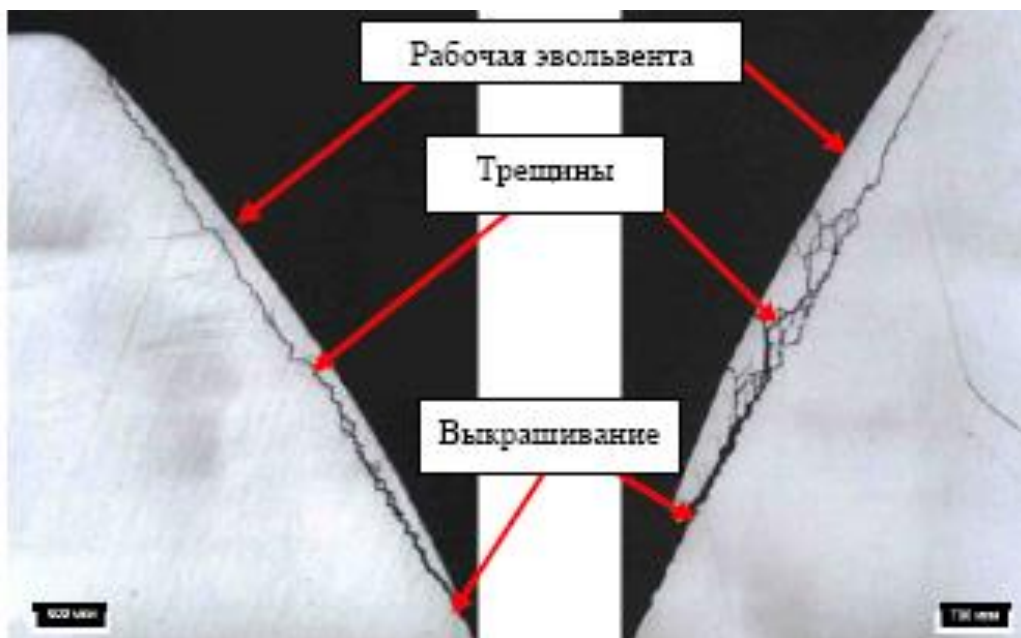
Макрошлифы рабочей стороны зуба шестерни в месте дефекта
